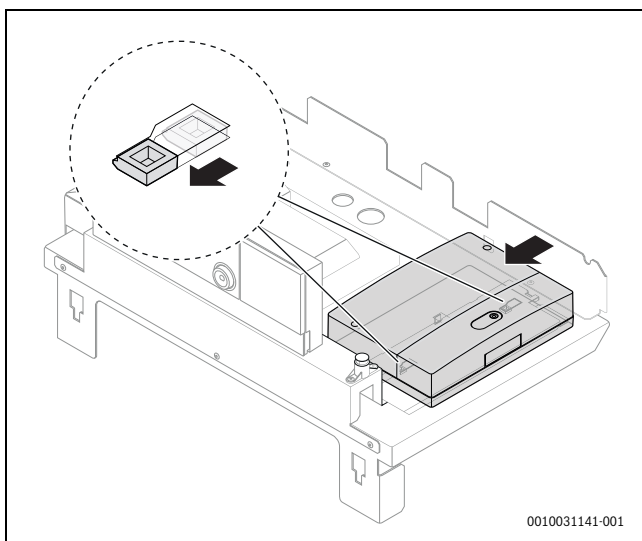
Montage des Elektronik-Moduls unter der Kesselhaube (Beispiel)
